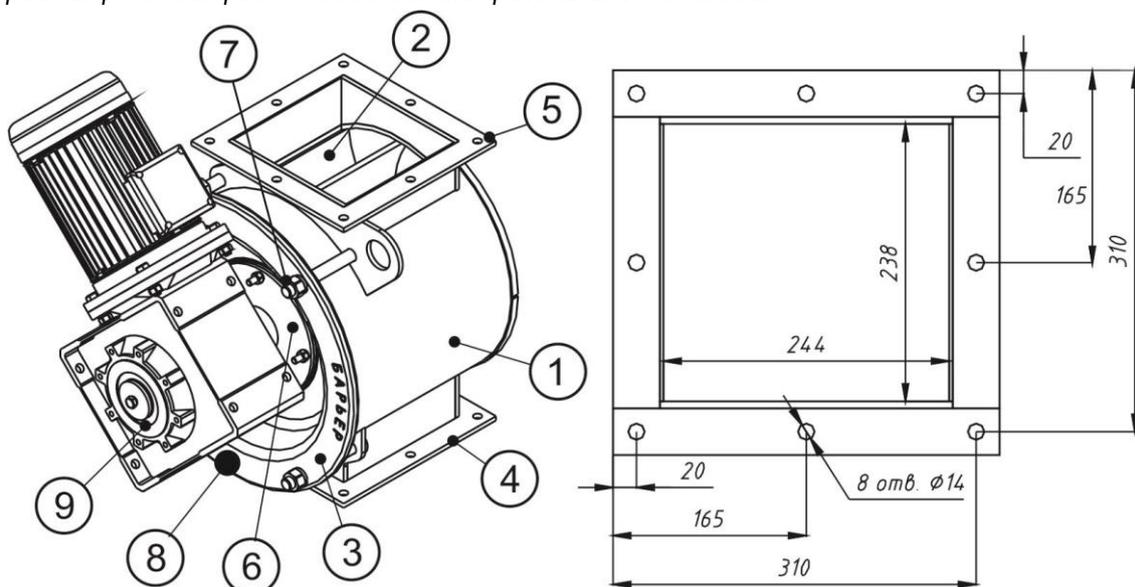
Внешний вид изделия, элементы регулирования, размеры присоединительных фланцев
